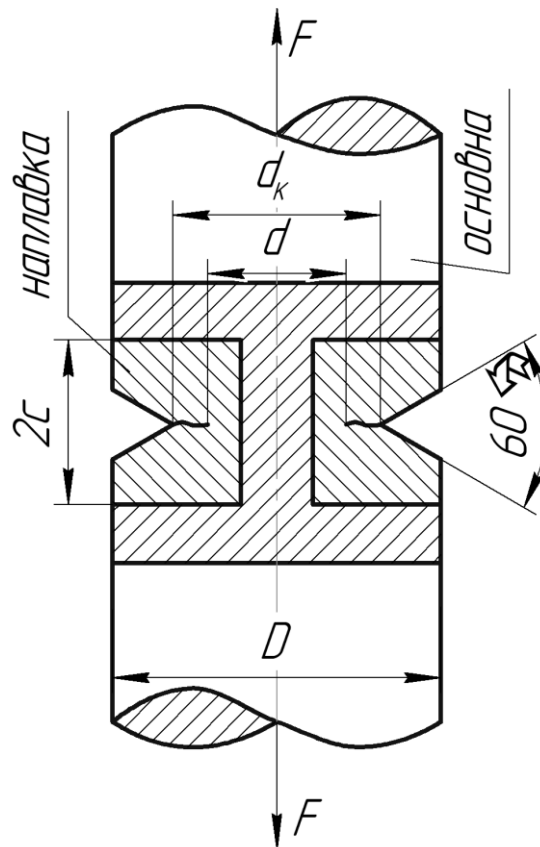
Схема осьового розтягу циліндричного зразка з кільцевою наплавкою
